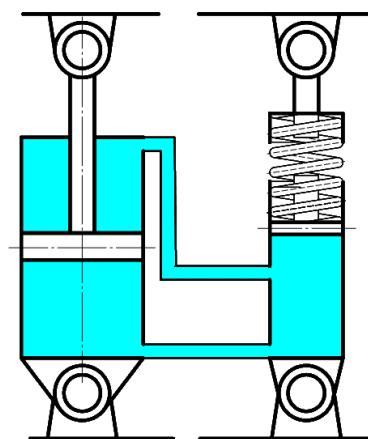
Гидроцилиндр с разными активными площадями поршней и компенсационным цилиндром
